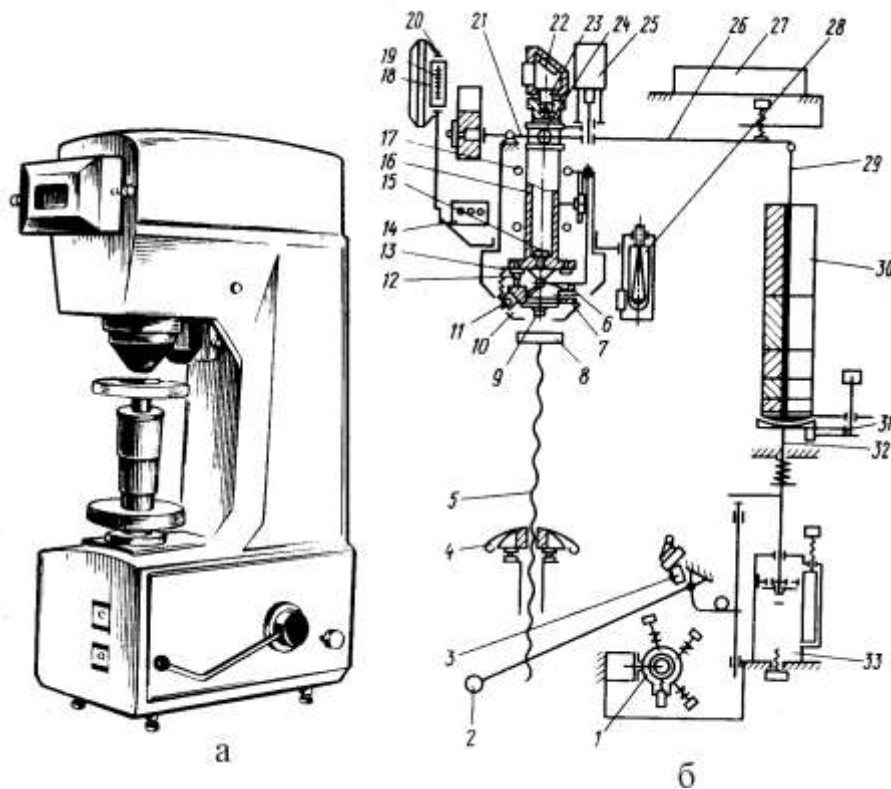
Прилад ТП-7Р-1 для вимірювання твердості металів за методом Віккерса: а – загальний вигляд; б – схема випробовування: 1 – реле часу; 2 – рукоятка; 3 – мікроперемикач; 4 – маховик; 5 – механізм піднімання; 6 – упор; 7 – каретка; 8 – предметний столик; 9 – об’єктив; 10 – чохол; 11 – наконечник; 12 – упор; 13 – пружина; 14 – лампочка; 15 – ахроматична лінза; 16 – шпindel; 17 – напрямівні; 18, 19 – шкали; 20 – мікрометрична головка; 21 – важіль; 22 – дзеркало; 23 – окуляр; 24 – підчіпники; 25 – магнет; 26 – важіль; 27 – панель з електроапаратурою; 28 – освітлювач; 29 – підвіска; 30 – вантажі; 31 – контакти; 32 – шток; 33 – демпфер
